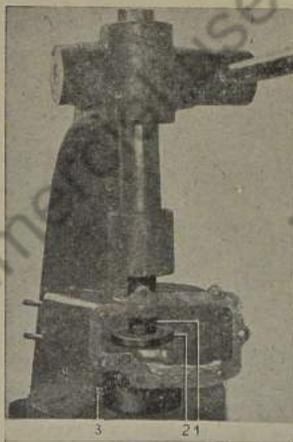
Zylinderrollenlager aus Zwischenradgehäuse herausdrücken
